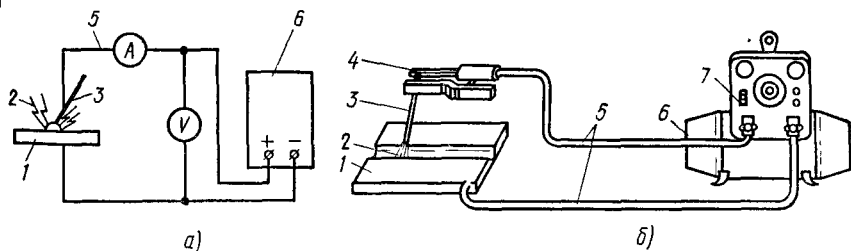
Схема питания дуги при ручной дуговой сварке (на постоянном токе): а — электрическая схема, б — общая компоновка поста для сварки; 1 — изделие, 2 — сварочная дуга, 3 — электрод, 4 — электрододержатель, 5 — сварочные провода, 6 — источник питания, 7 — щит с приборами контроля и регулирования параметров режима сварки
